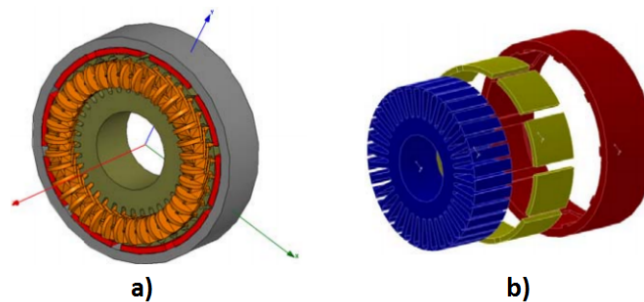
Gerador de ímãs permanentes de fluxo radial com rotor externo. a) Vista Compacta, b) Vista Explodida.
